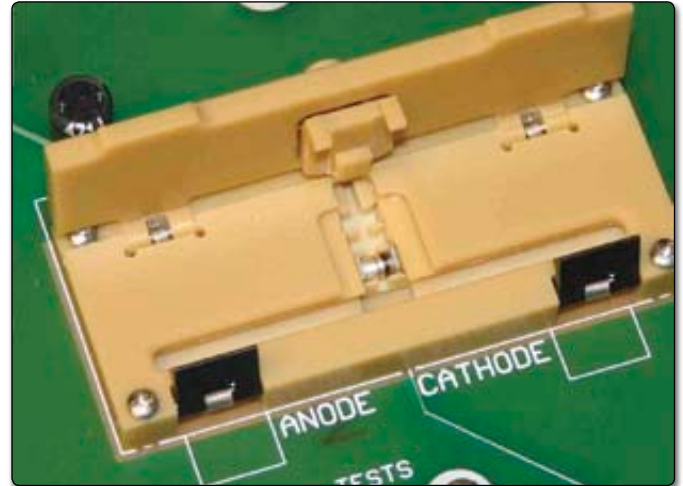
Test-jig contact für die Kontaktierung von Dioden im SQ-MELF-Gehäuse
